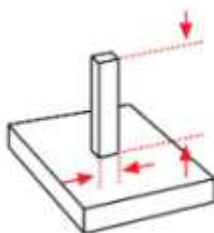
Smjernica za oblikovanje 3D printanih dijelova (5) [16]
